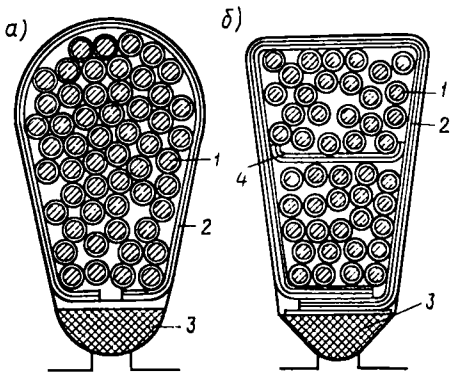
Пазы статора для всыпных однослойной (а) и двухслойной (б) обмоток:
